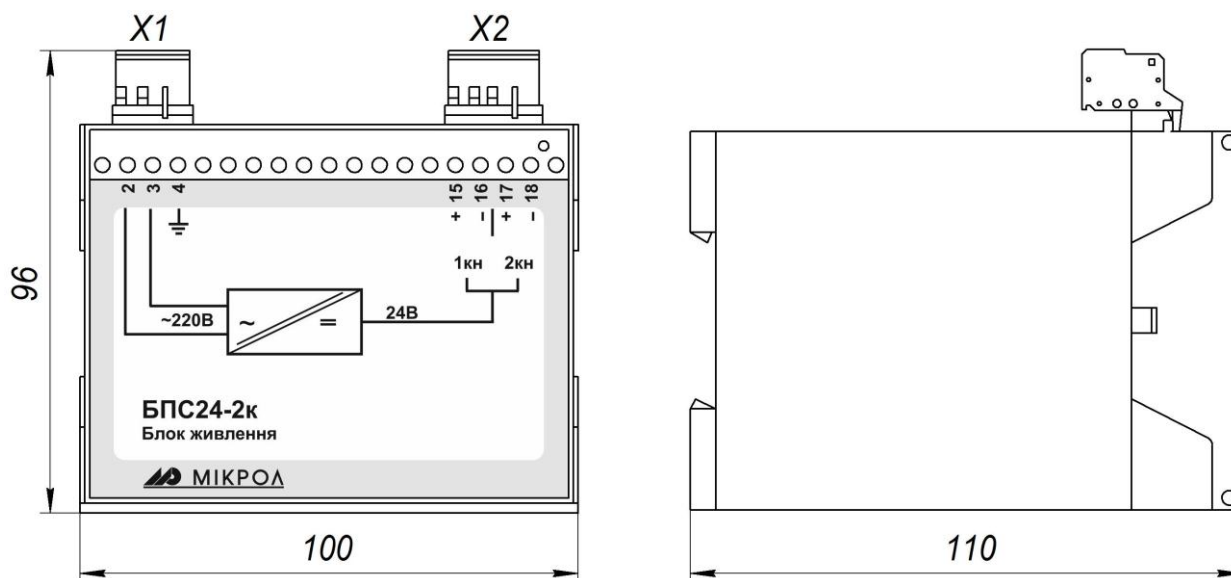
Внешний вид и габаритные размеры блока БПС24-2к
